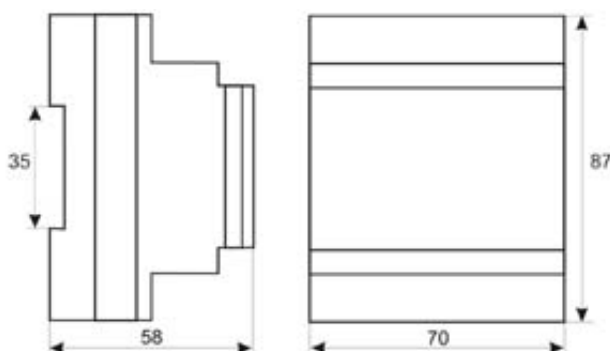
Габаритные размеры и внешний вид прибора БПР 24/12
